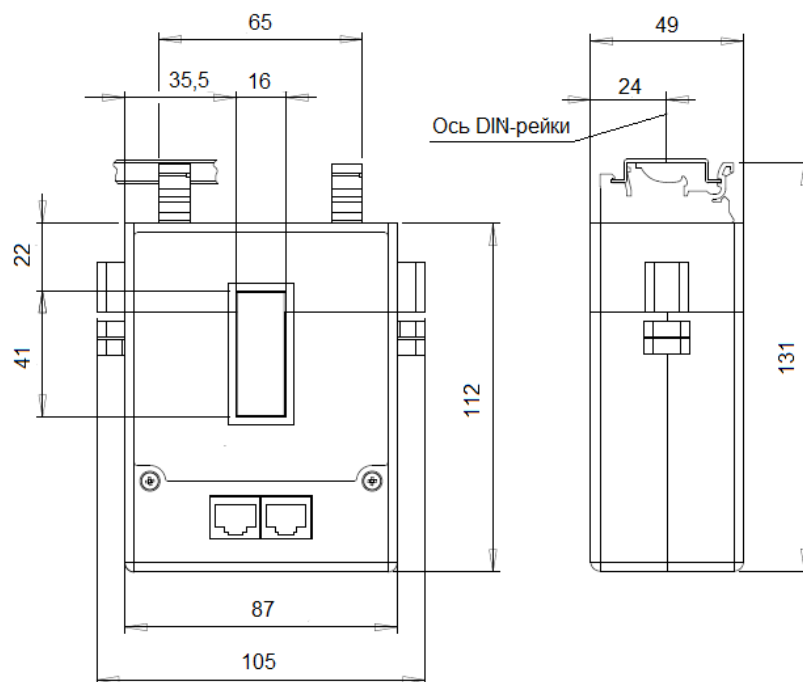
Габаритные и установочные размеры ИДП-193и-X₁.X₂.RS
